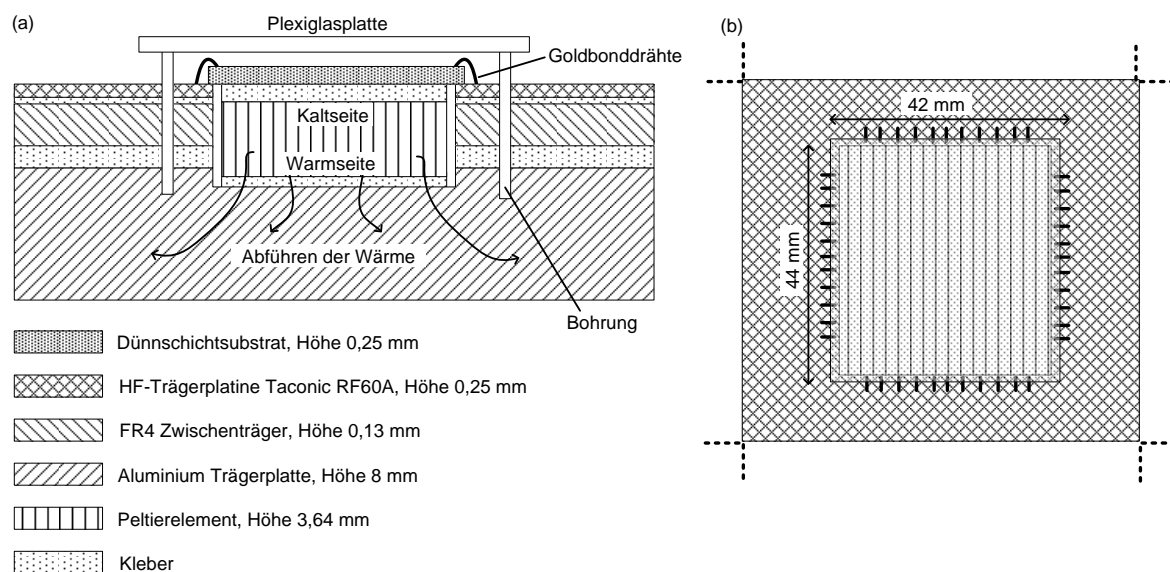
(a) Querschnitt und (b) Sicht auf die Komplettmontage des Wandlermoduls.
